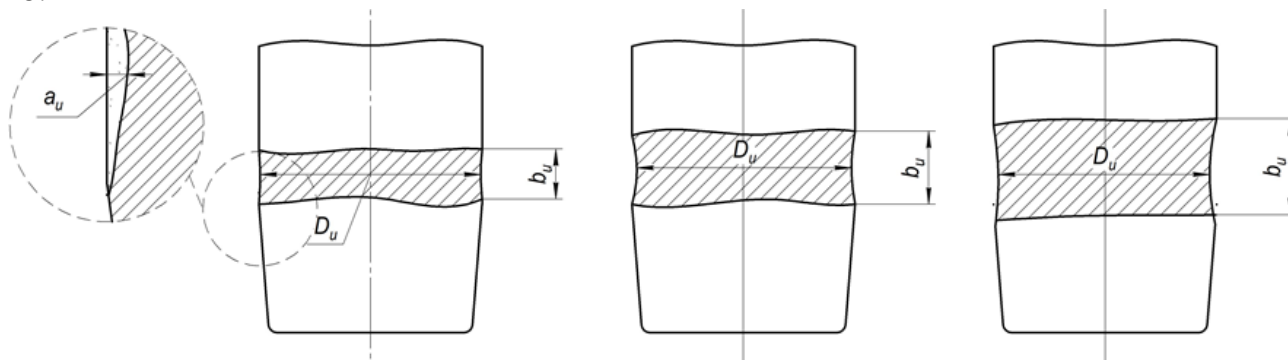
Схема износа рабочей поверхности штампового инструмента:
